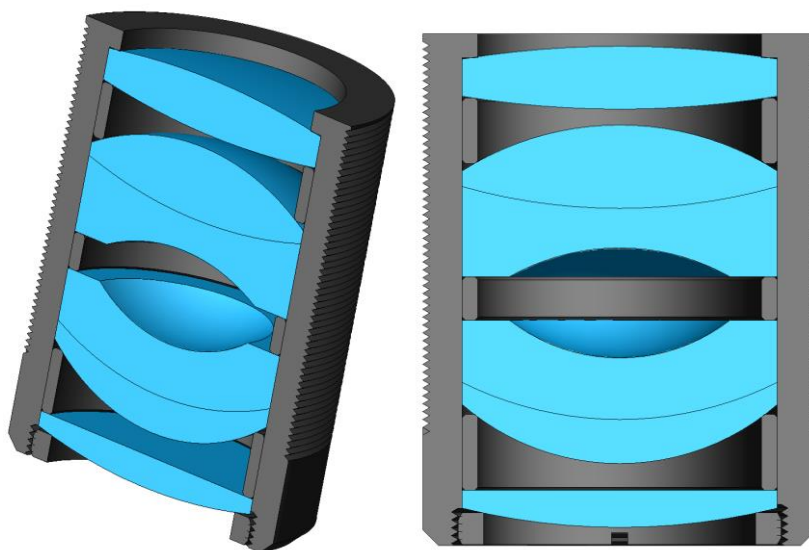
Vista 3D de la lent de camp (esquerra) i una secció frontal (dreta).
